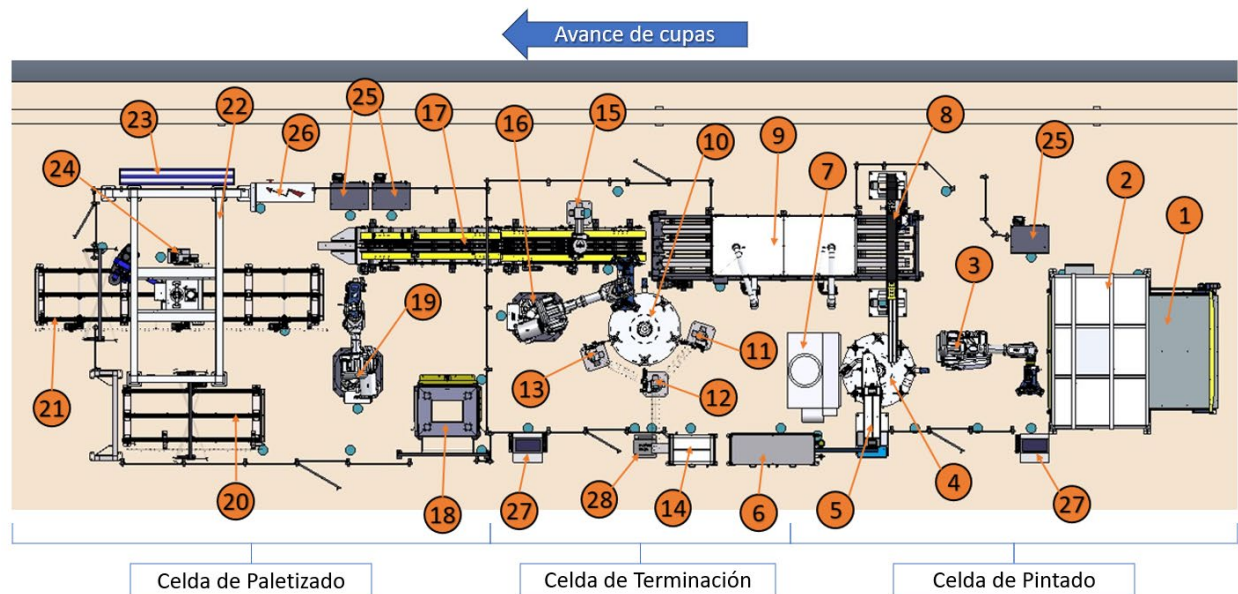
Detalle de equipos - Vista en planta FOL3.
